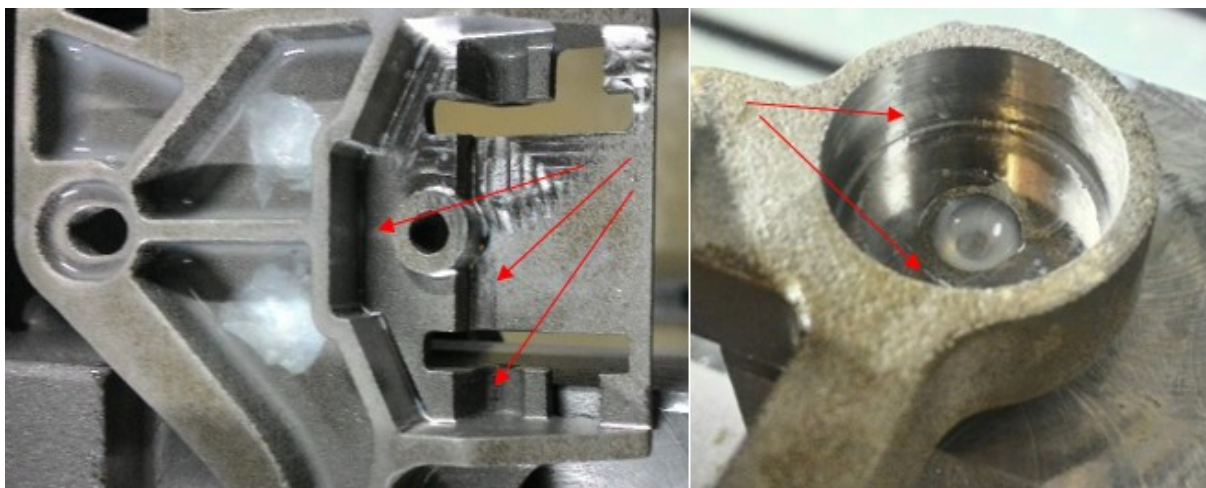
Příklad obrábění rámečku vysokorychlostním vřetenem kulovou frézou D 0,5 mm, M45785.050
